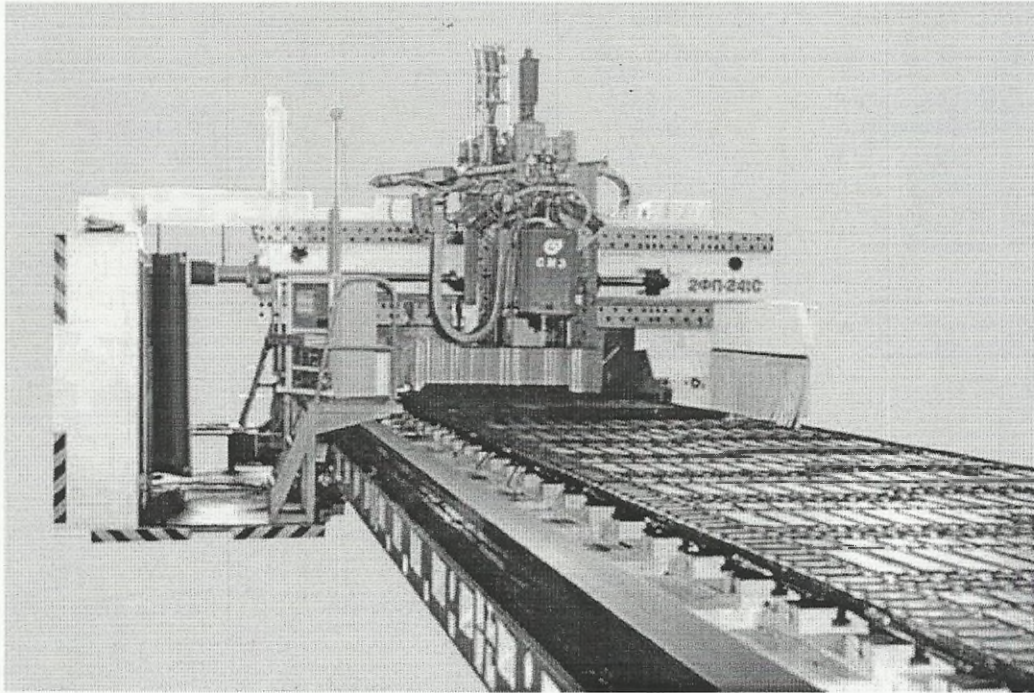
Загальний вигляд фрезерного верстата моделі 2ФП-241 з ЧПУ
